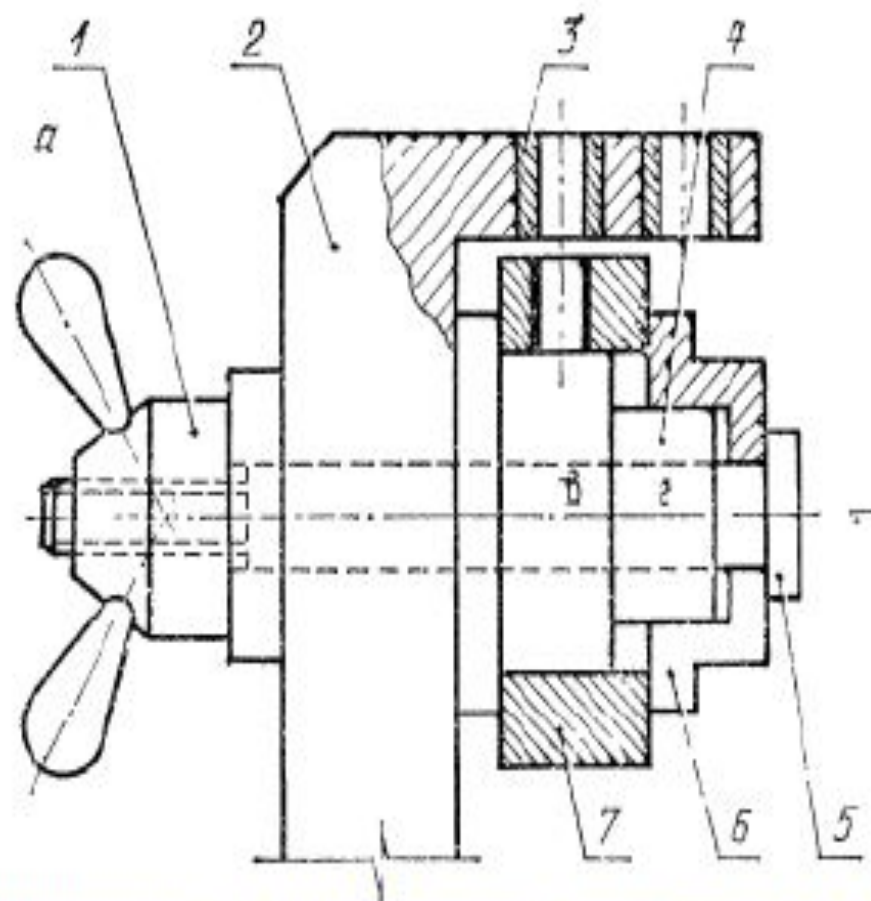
Специализированный безналадочный кондуктор для групповой обработки
